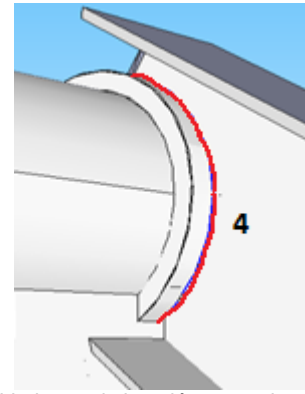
Soldadura 4 de la unión entre el anclaje y la torre (Elaboración propia, SketchUp)
